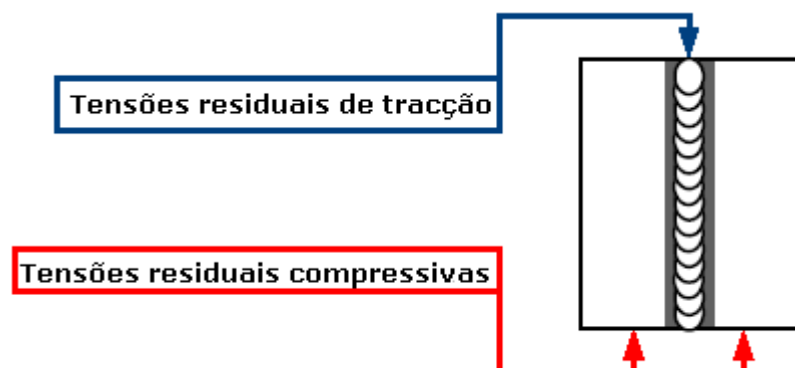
Tipo de tensões residuais no cordão de soldadura e afastado deste [13].
